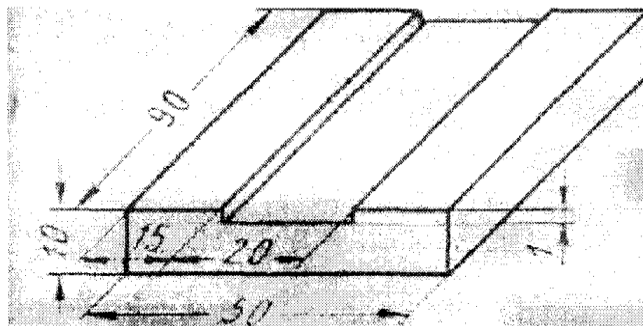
Подготовка канавки на поверхности стальной пластины, наплавляемой сормайтом
